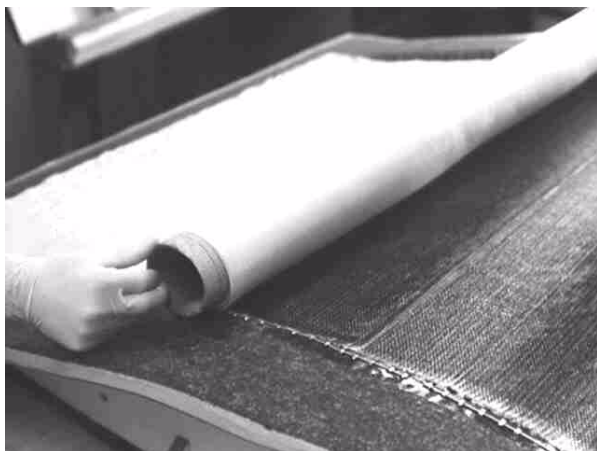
163-g/m²-Glasgewebe als erste Isolierung
